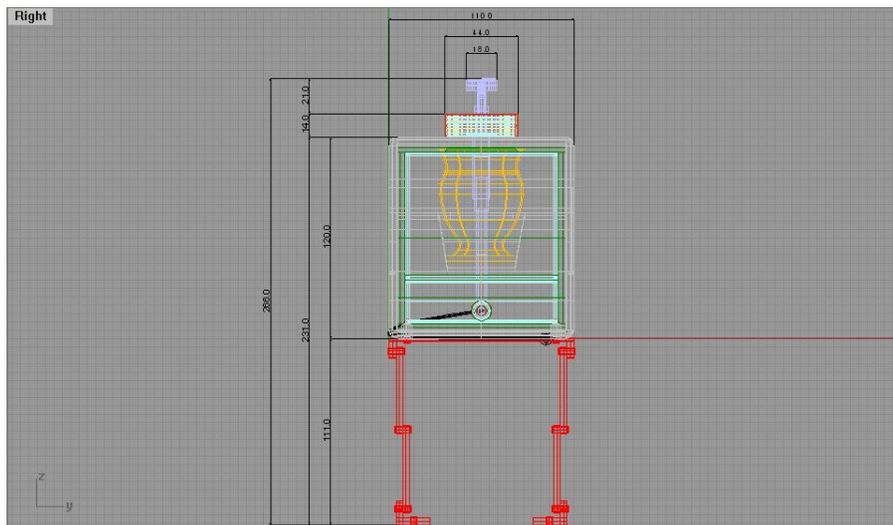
Vista frontal del producto final 1:1 en mm.
